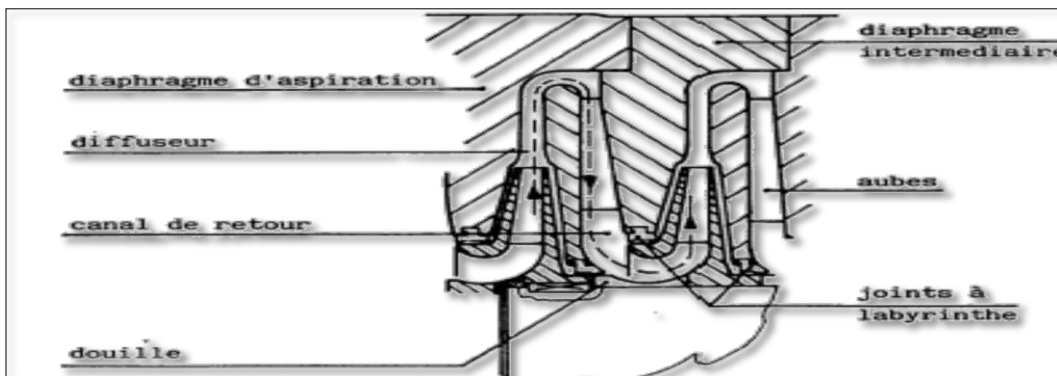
Aspiration du gaz d'un compresseur centrifuge
